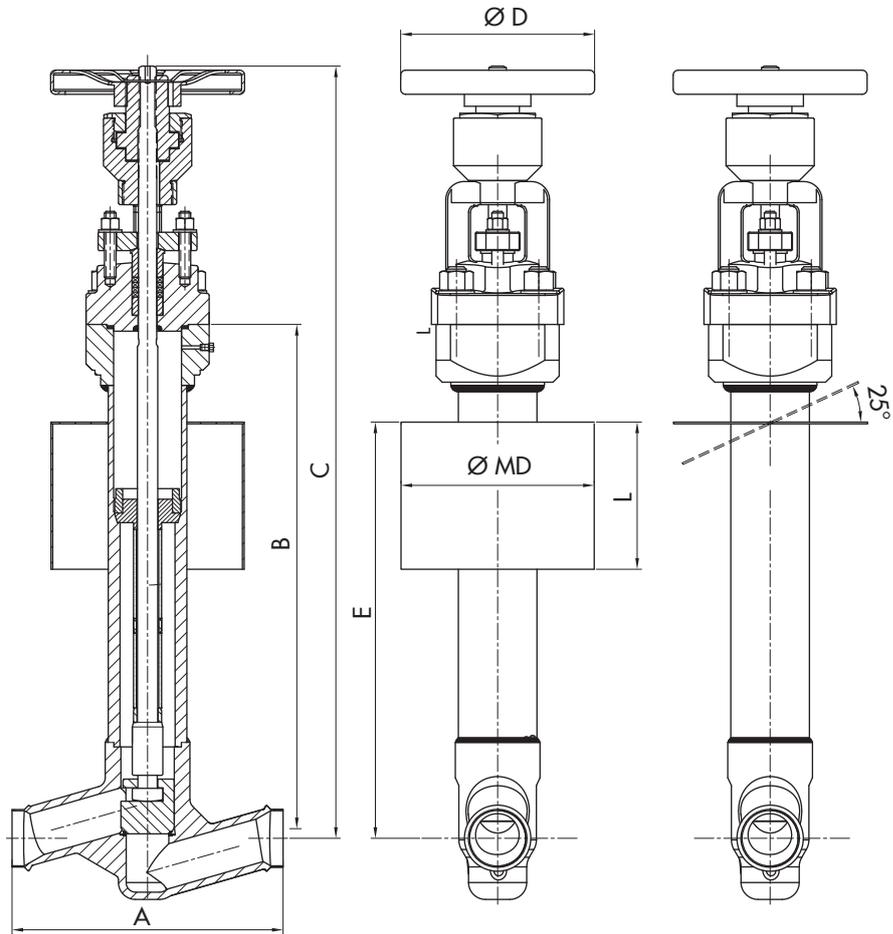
Durchgangsventil Typ 3588, Nennweite NPS 1/2...2 · Darstellung rechts: Kryoausführung
